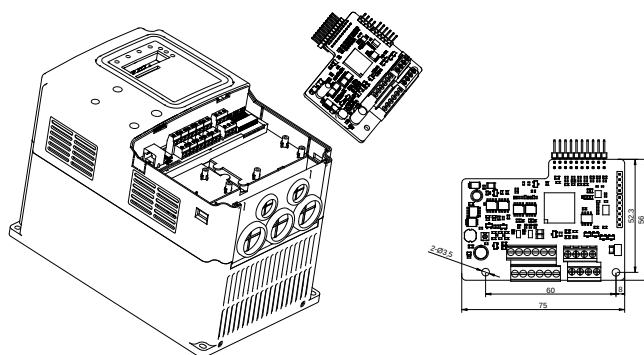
Размеры и схема установки EC-PG102-05-T
